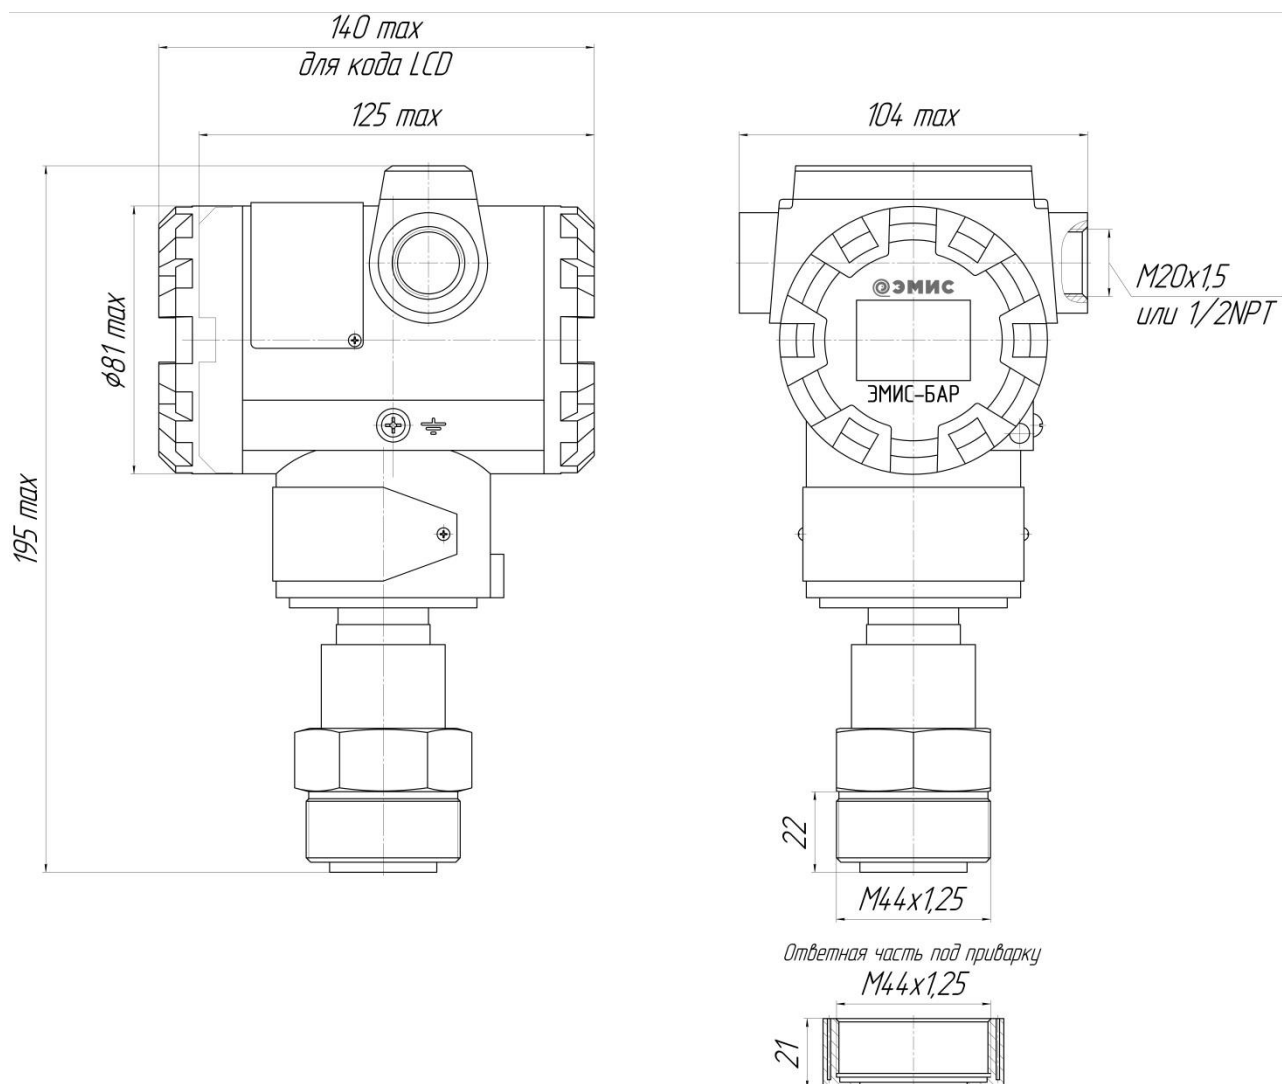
Габаритные и присоединительные размеры штуцерного исполнения с открытой мембраной датчиков давления ЭМИС-БАР 113
